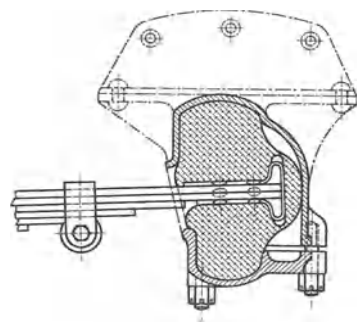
In Gummi gelagertes Ende einer Kraftwagenfeder.
